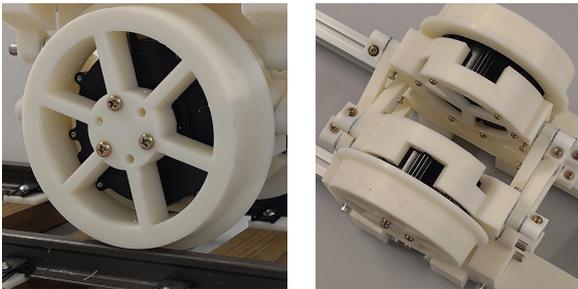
駆動ユニット. インホイール形式としており、アクチュエータの半分を覆うような車輪と、アクチュエータをサスペンションを介して車体フレームと連結するケーシングからなる. Drive unit. A cup shaped wheel with in-wheel intelligent actuator, supported by suspension unit fixed on the body frame.
